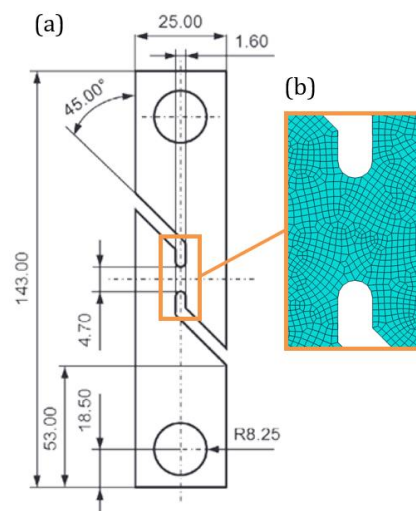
23: Maillage des éprouvettes de cisaillement. (a) dimension de l'éprouvette, (b) éprouvette 6082-T4, taille de maille = 0,2 mm.
